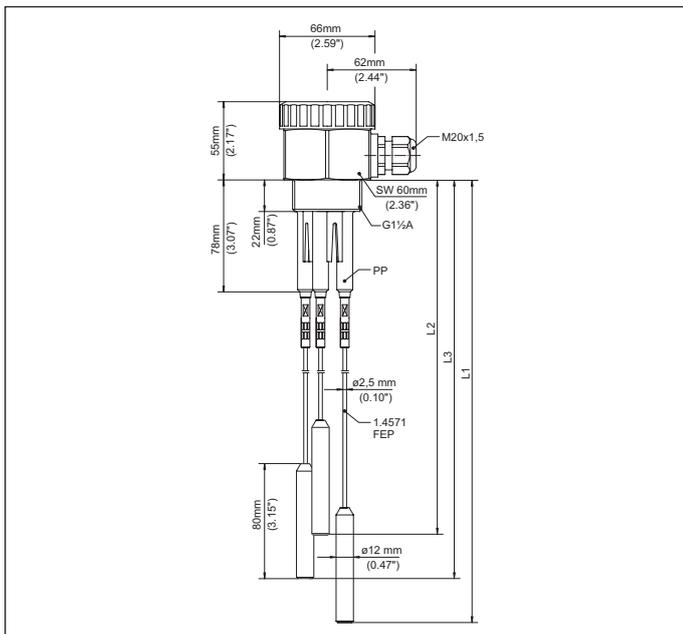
Sonda condutiva de medição com vários cabos de aço EL 6
